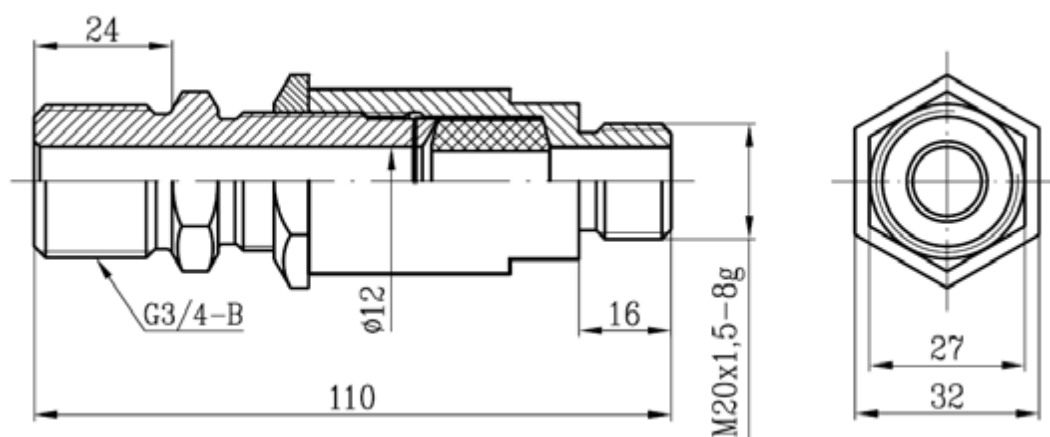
Ввод кабельный для трубного монтажа (ТБ 3/4")
